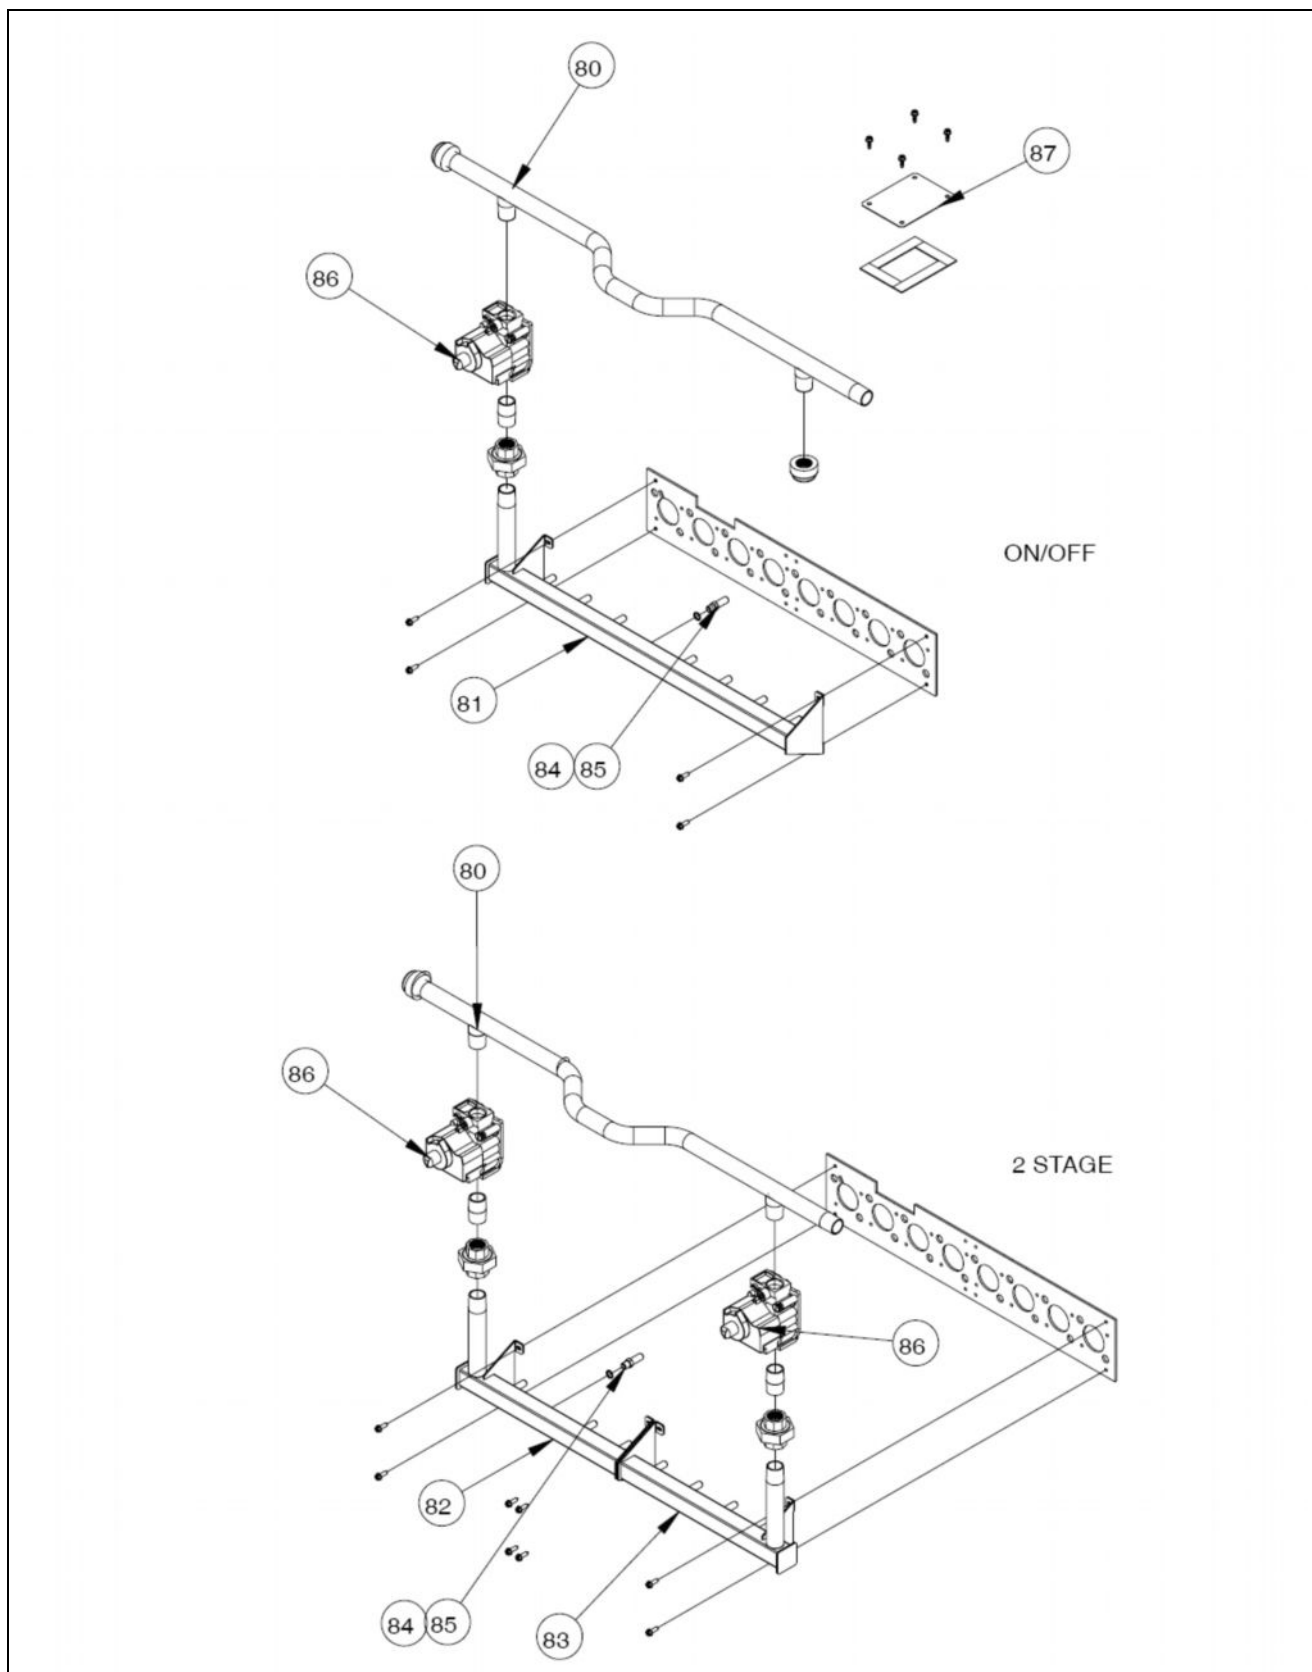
Детали газового тракта Пеннант, типоразмеры 200 - 400.
